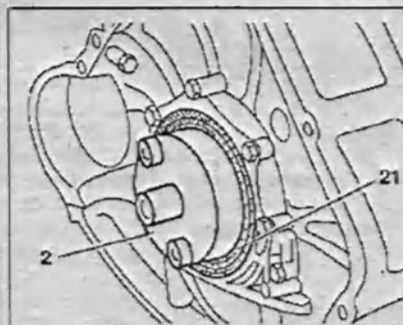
Установите внутреннюю часть приспособления 2 на коленчатый вал.
